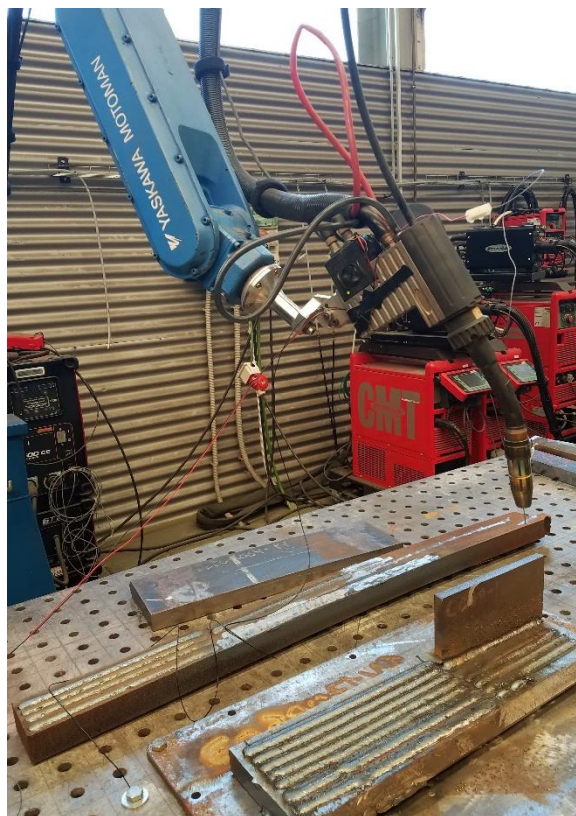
Montaje del sistema de medida de tensión entre la punta del soldador y la masa de la pieza
